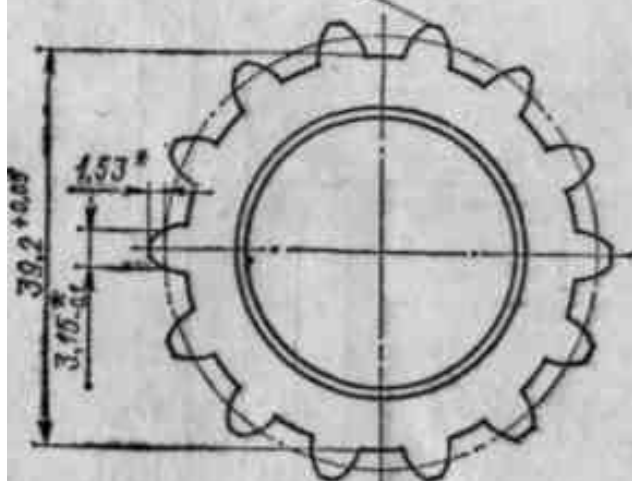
Зубчатое колесо IV передачи вторичного вала
